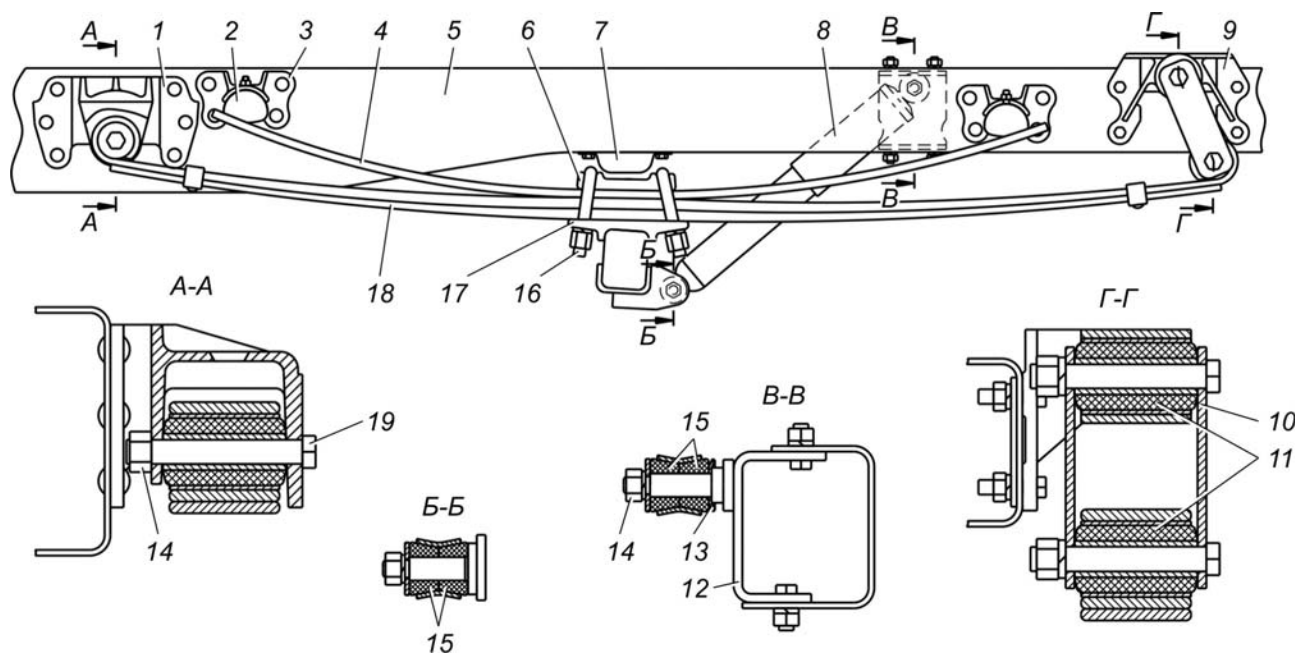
Задняя подвеска автомобилей типа 4x2 (кроме автобусов и ГАЗ-32214): 1, 2, 9 и 12 – кронштейны; 3 – подушка дополнительной рессоры; 4 – подрессорник; 5 – лонжерон рамы; 6 – накладка; 7 – буфер; 8 – амортизатор; 10 – серьга; 11 – резинометаллические шарниры; 13 – шайба; 14 – гайка; 15 – резиновые втулки; 16 – стремянка; 17 – подушка; 18 – рессора; 19 – болт
